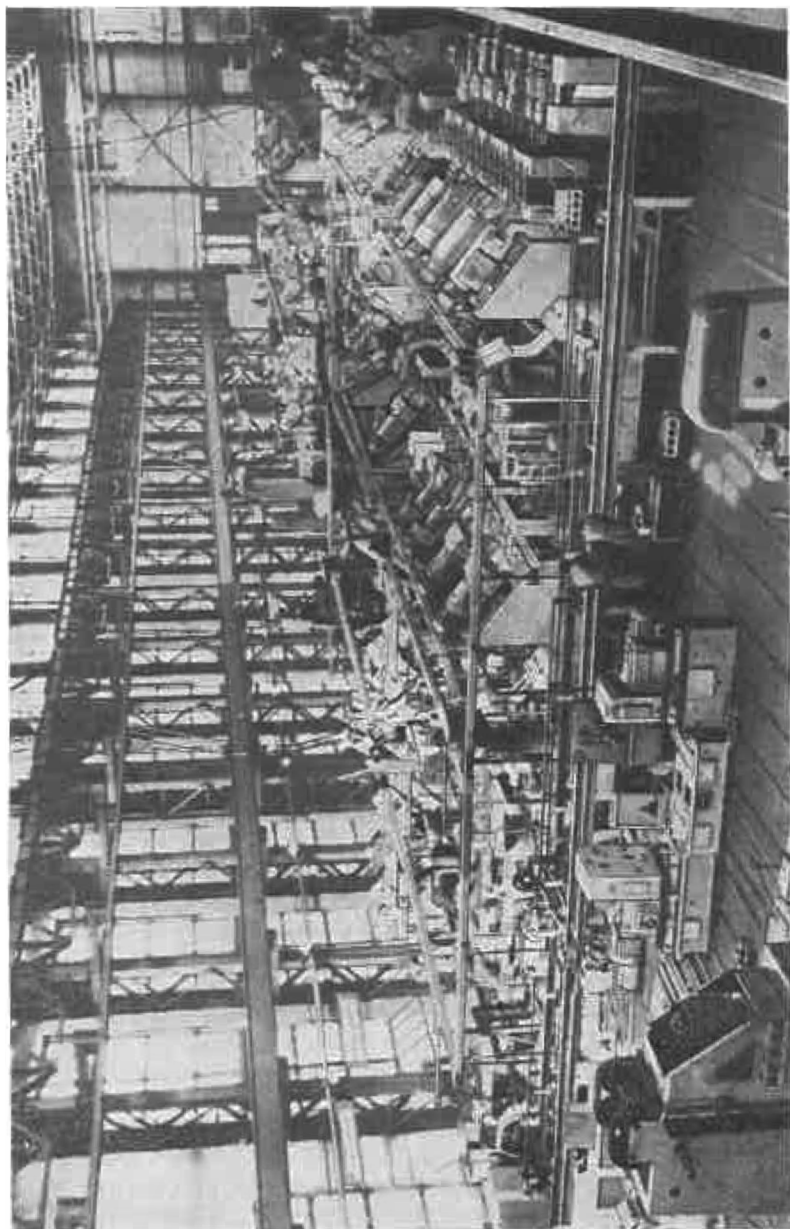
Vue d'ensemble d'un atelier moderne
